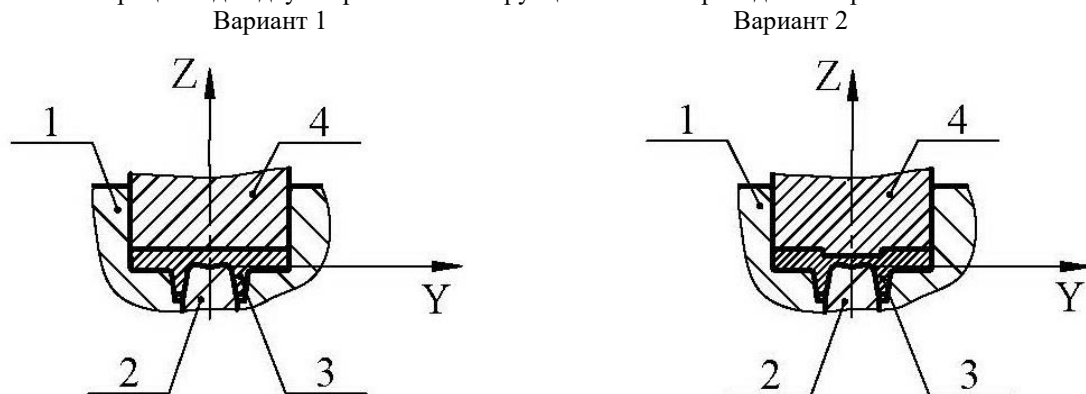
Схема процесса закрытой объемной штамповки фланца.
